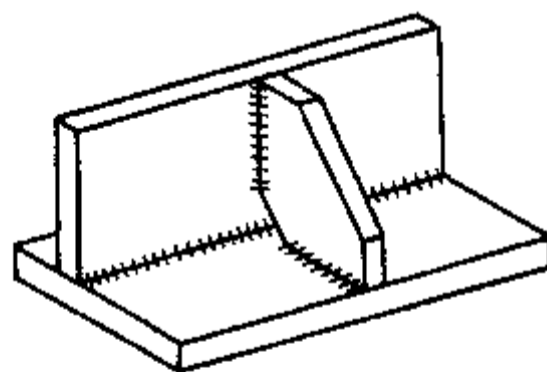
焊缝交叉处加强肋的合理结构
